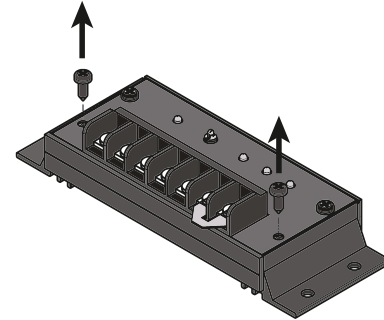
Entfernen der 2 Schrauben der Blende.
